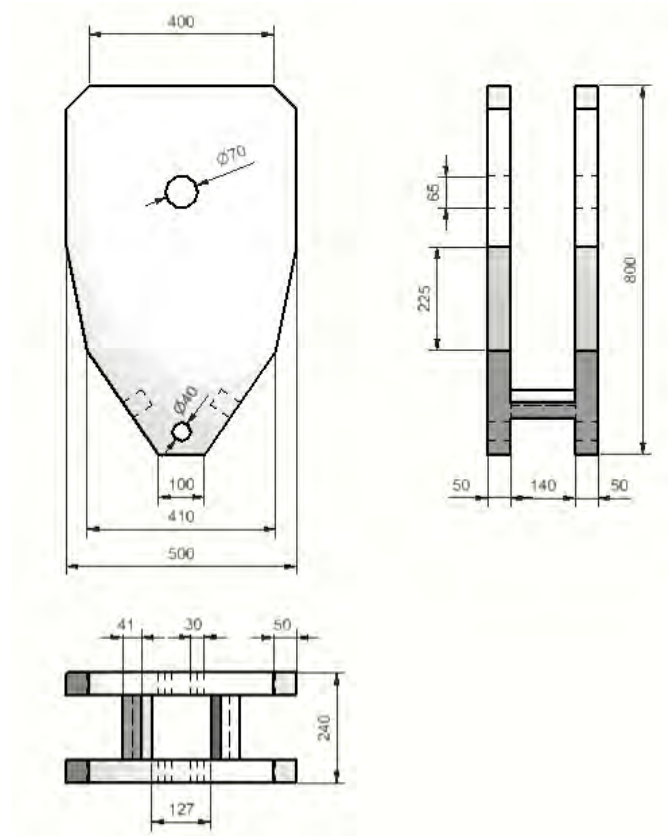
Dimensionet e pllakëve ku lidhet çengeli.
